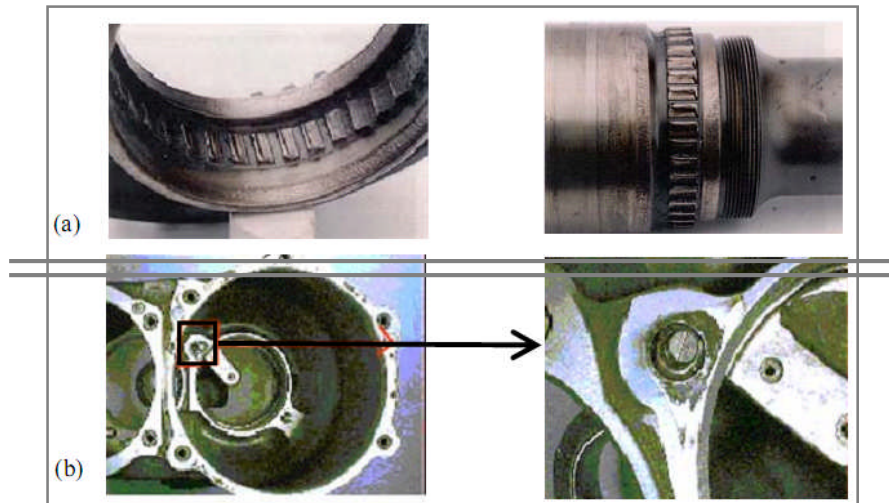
Quelques cas d'usure en fretting de pièces assemblées :
